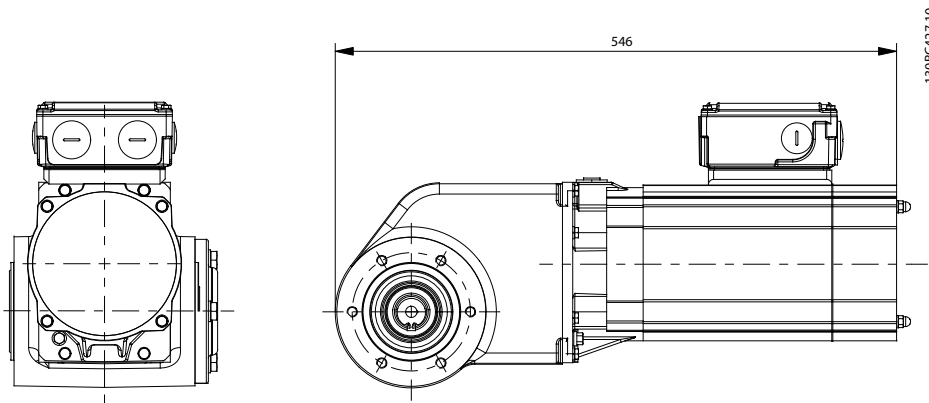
带机械制动选件的 VLT® OneGearDrive 的尺寸
